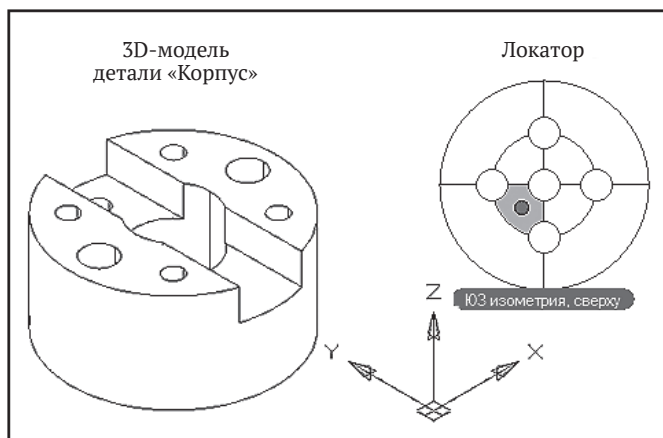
Окончательный вид 3D-модели детали «Корпус» в ЮЗ изометрии
